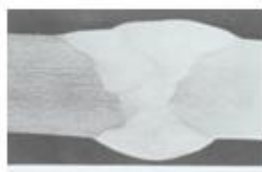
良好多道 MIG 对接焊缝示例
